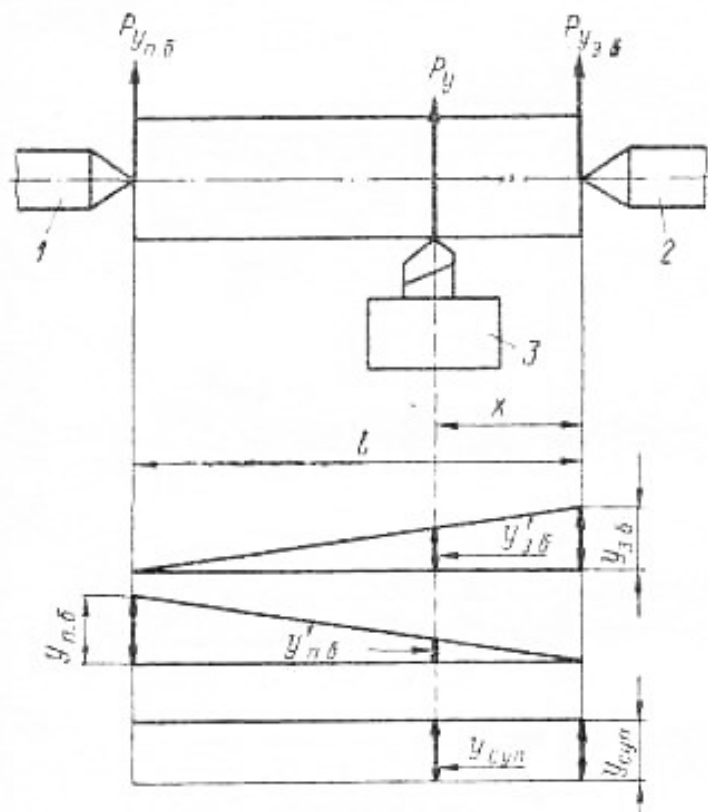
Схема навантаження і пружних деформацій вузлів токарного верстата при обробленні вала в центрах: 1 – передня бабка; 2 – задня бабка; 3 – супорт
